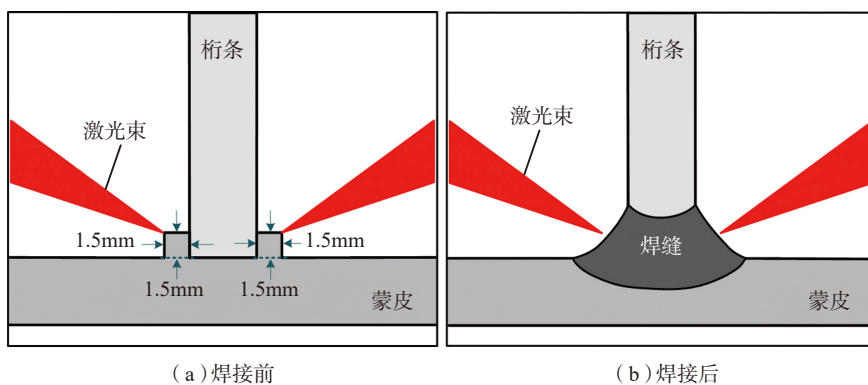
预置双小凸台蒙皮-桁条T型焊接结构示意图
